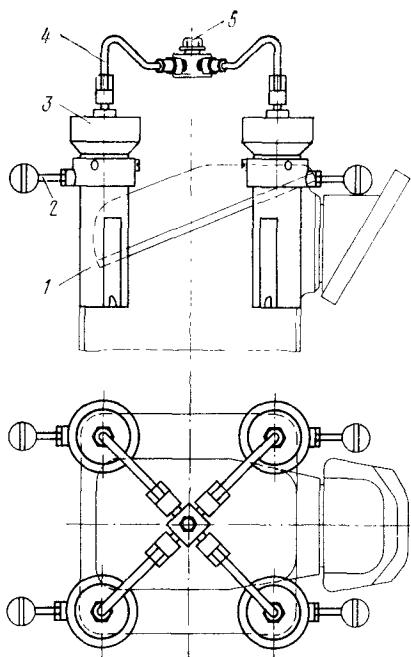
Приспособление для гидро-затяжки шпилек крепления комплексов к блоку:
